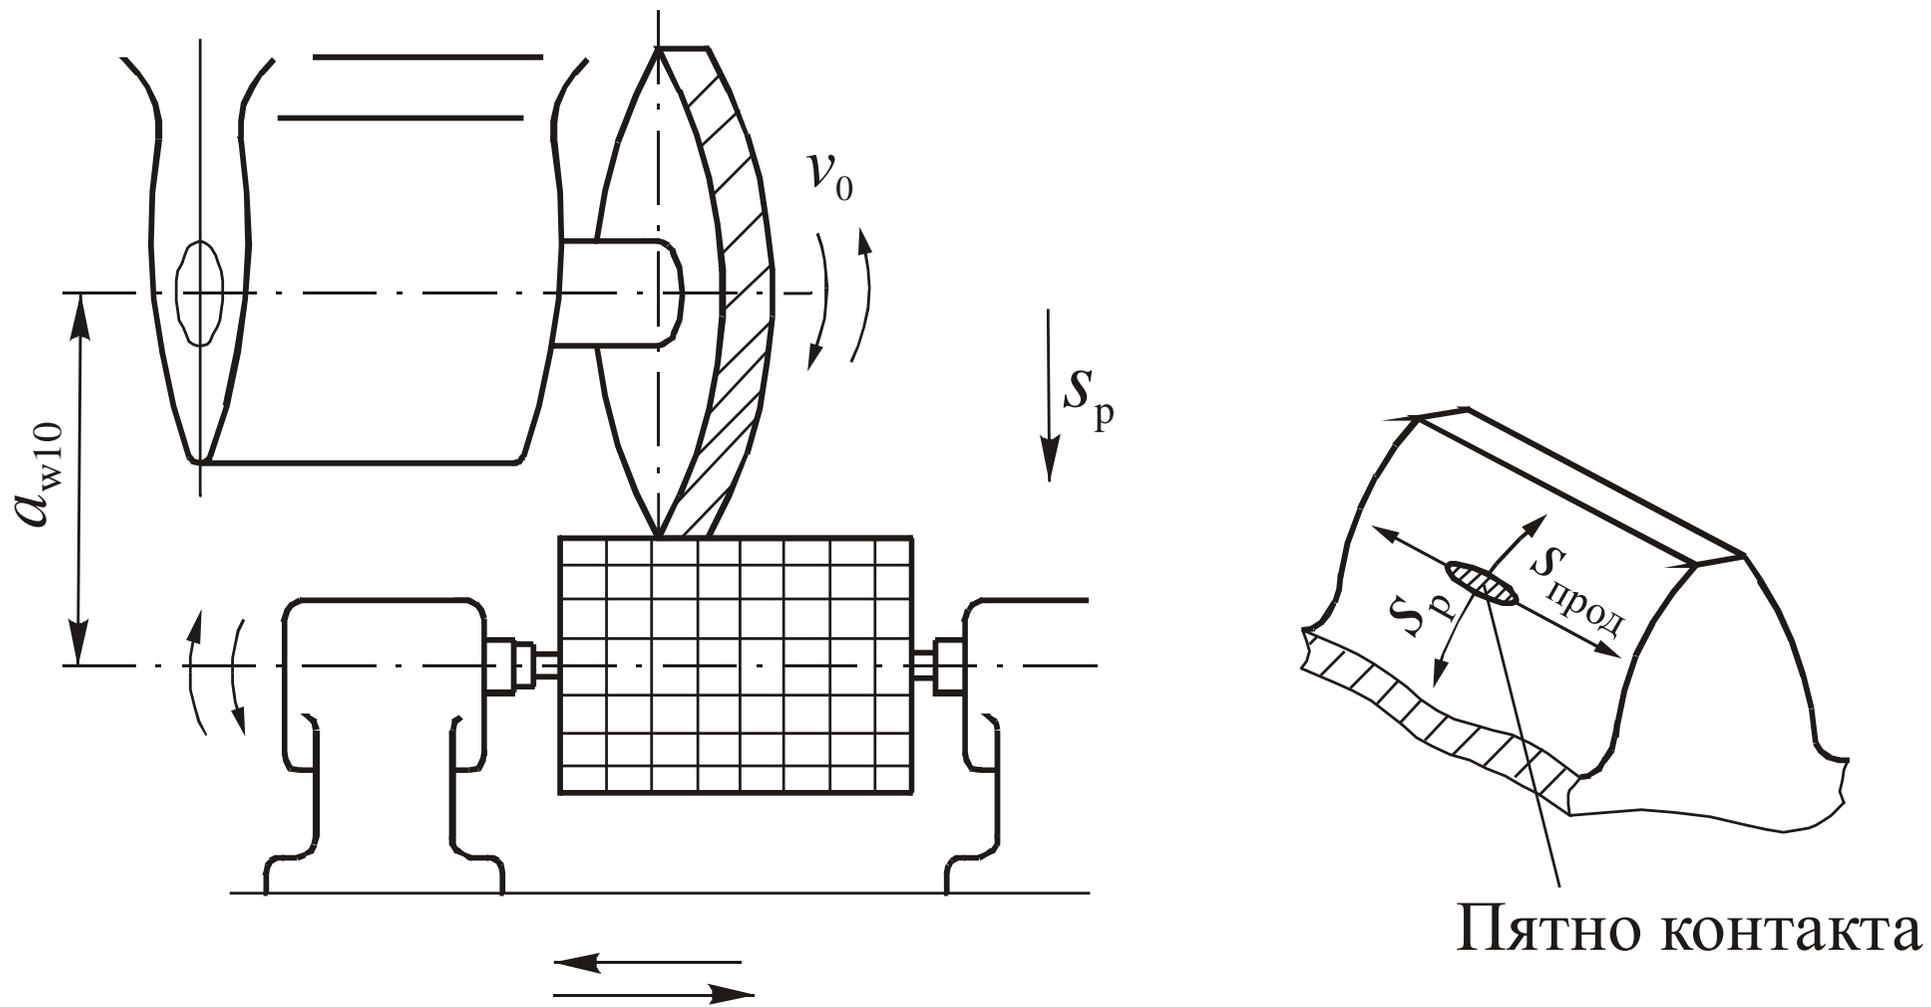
Установка на станке шевера и обрабатываемого колеса
